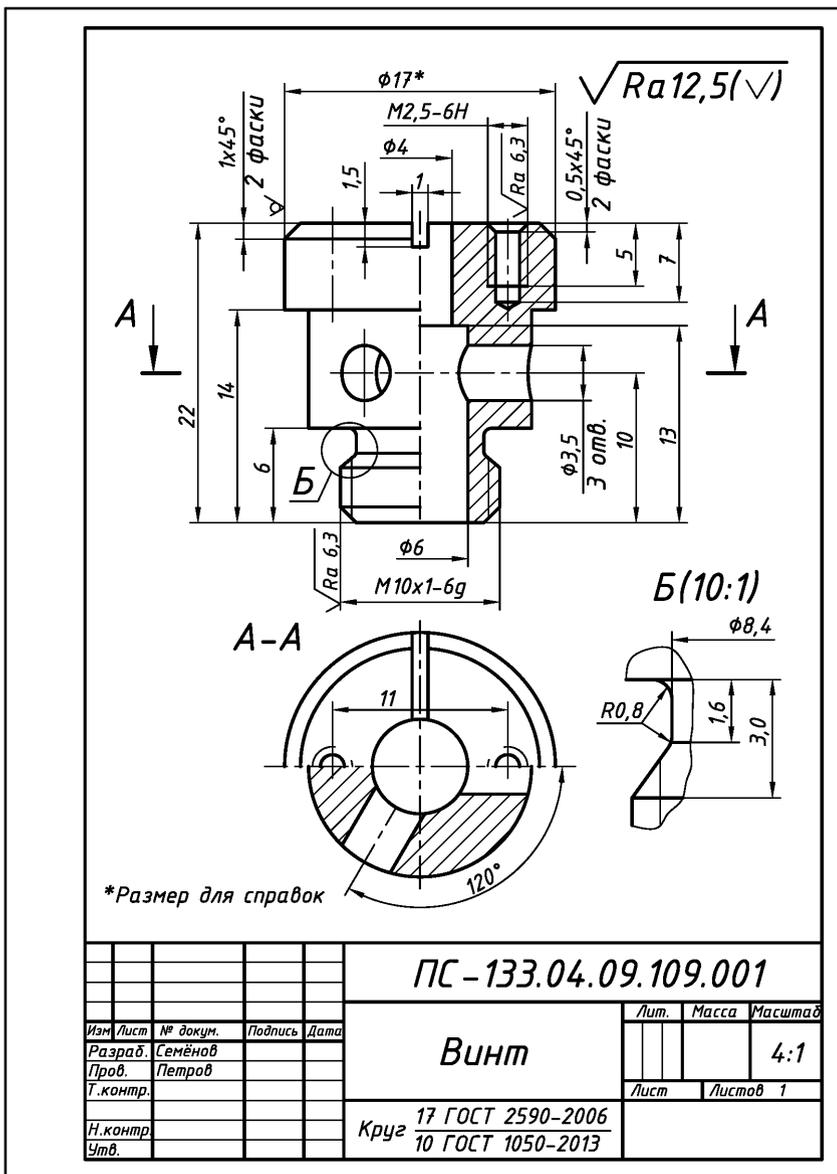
Оформление рабочего чертежа точеной детали из металла
